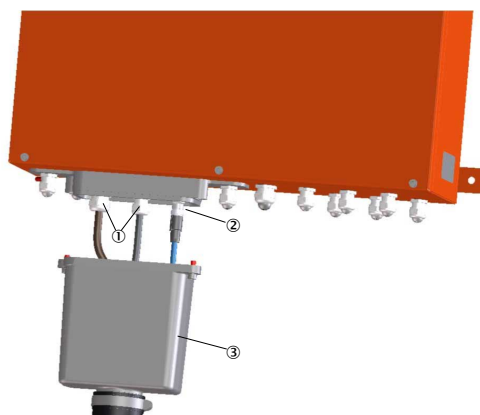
Соединительный шланг приемопередающий блок/ блок управления
